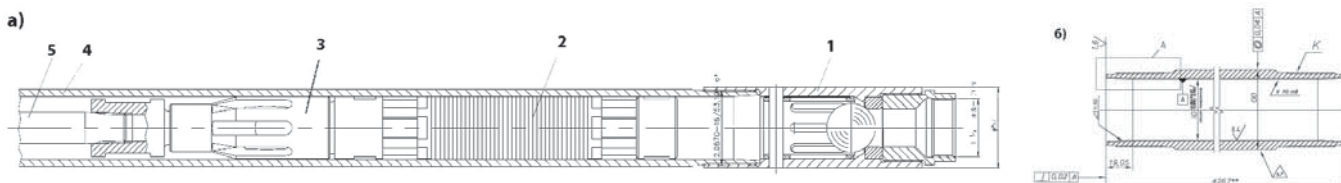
Противопесочный штанговый глубинный насос: а – общий вид насоса; б – цилиндр насоса; 1 – всасывающая клапанная камера; 2 – уплотнительные элементы плунжера; 3 – плунжер; 4 – цилиндр насоса; 5 – штанга
